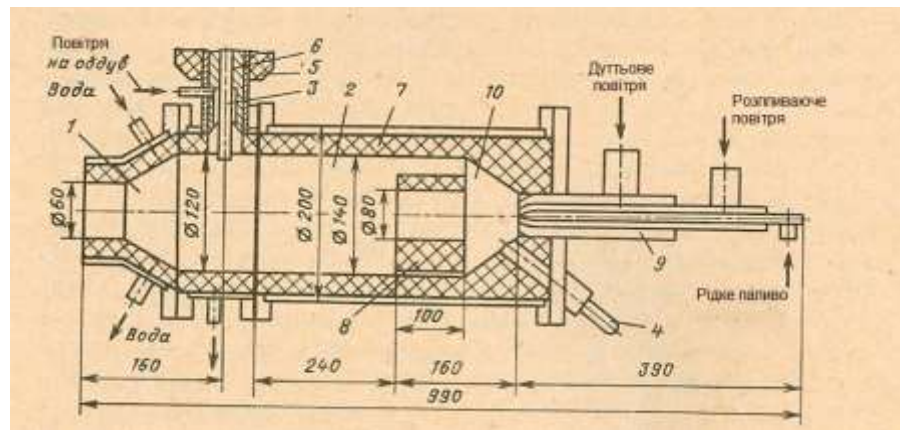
Схема електрорідиннопаливного пальника: 1 - сопло; 2 - камера згоряння; 3 - фазний електрод; 4 - запальний пристрій; 5 - гільза; 6 - корпус сальника; 7 - вогнетривка футеровка; 8 - рециркуляційна вставка; 9 – форсуночний пристрій; 10 – форкамера.[2].
